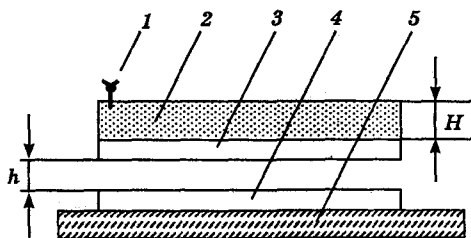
Схема сварки взрывом с параллельным расположением пластин
